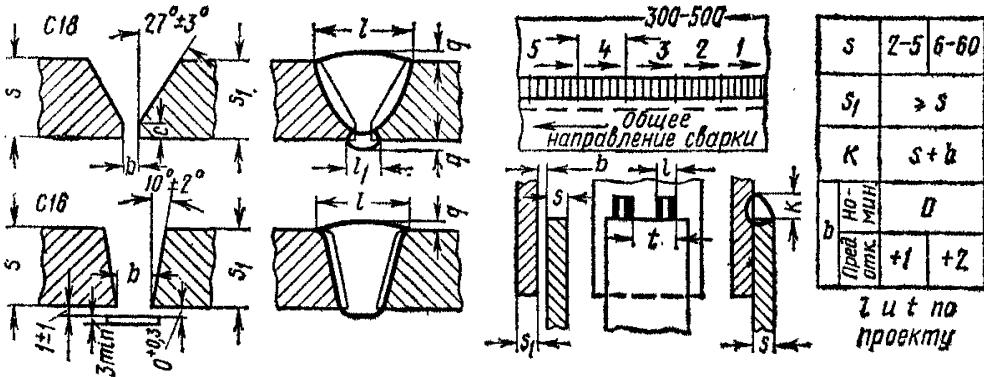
Типы швов при ручной дуговой сварке и последовательность сварки
